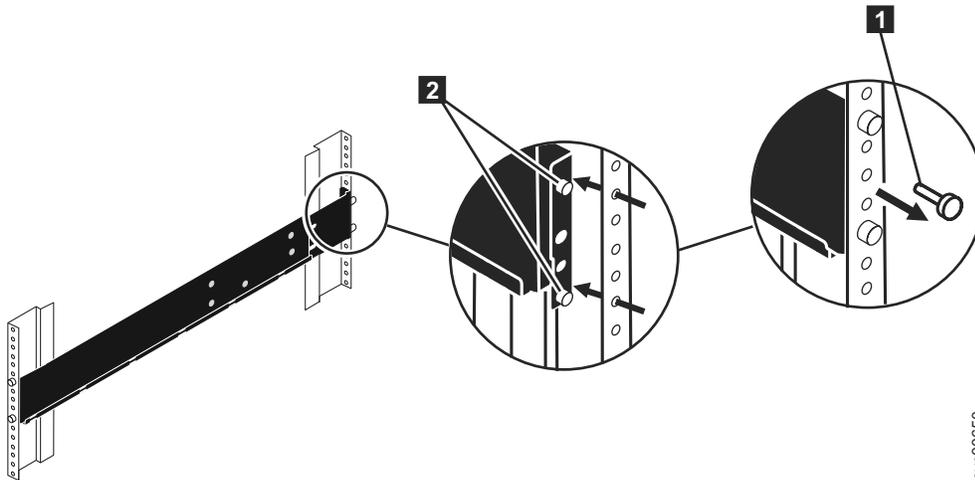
Removendo uma montagem de trilho a partir de um gabinete do rack
